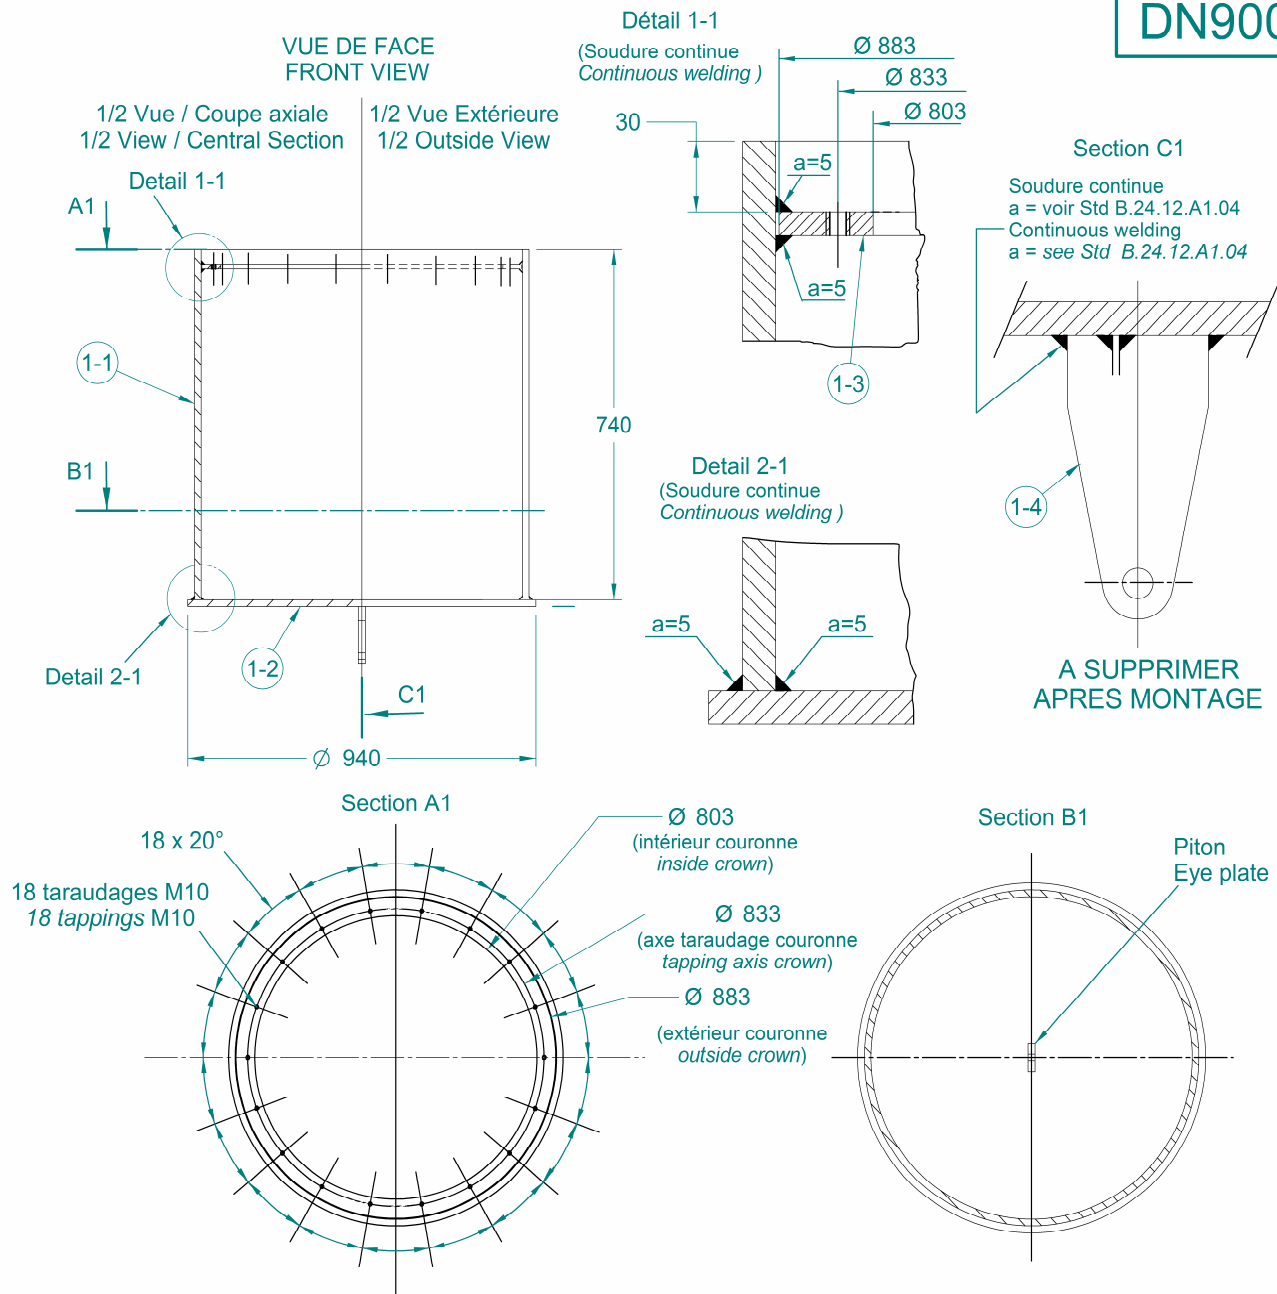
DETAILS PIECE REP.3 (PLAQUE D'ASSECHEMENT ET CONROLEUR (SUITE))
